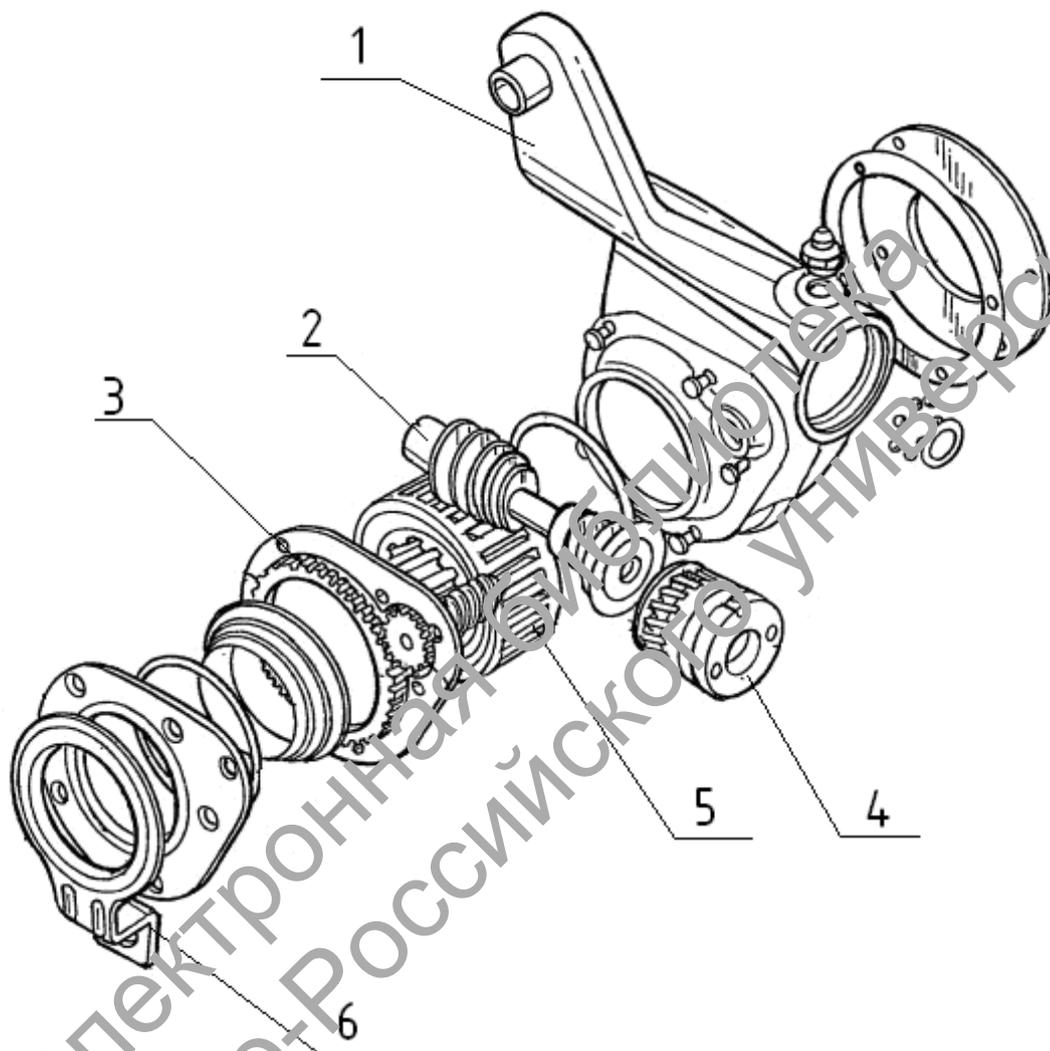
Автоматический регулятор зазора тормозных колодок, встроенный в тормозной рычаг: 1 – рычаг; 2 – червячный вал; 3 – зубчатая передача; 4 – регулировочное устройство; 5 – червячное колесо; 6 – опорное плечо
